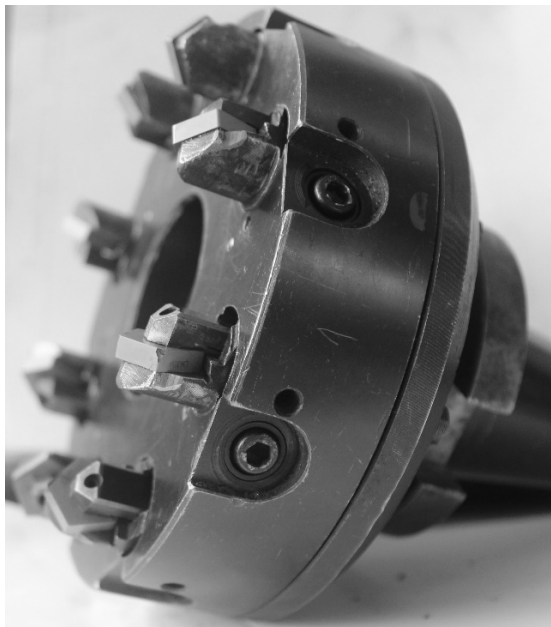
Экспериментальный образец блочно-модульной торцевой фрезы с установкой блока резцового по цилиндрической поверхности с упором в буртик
